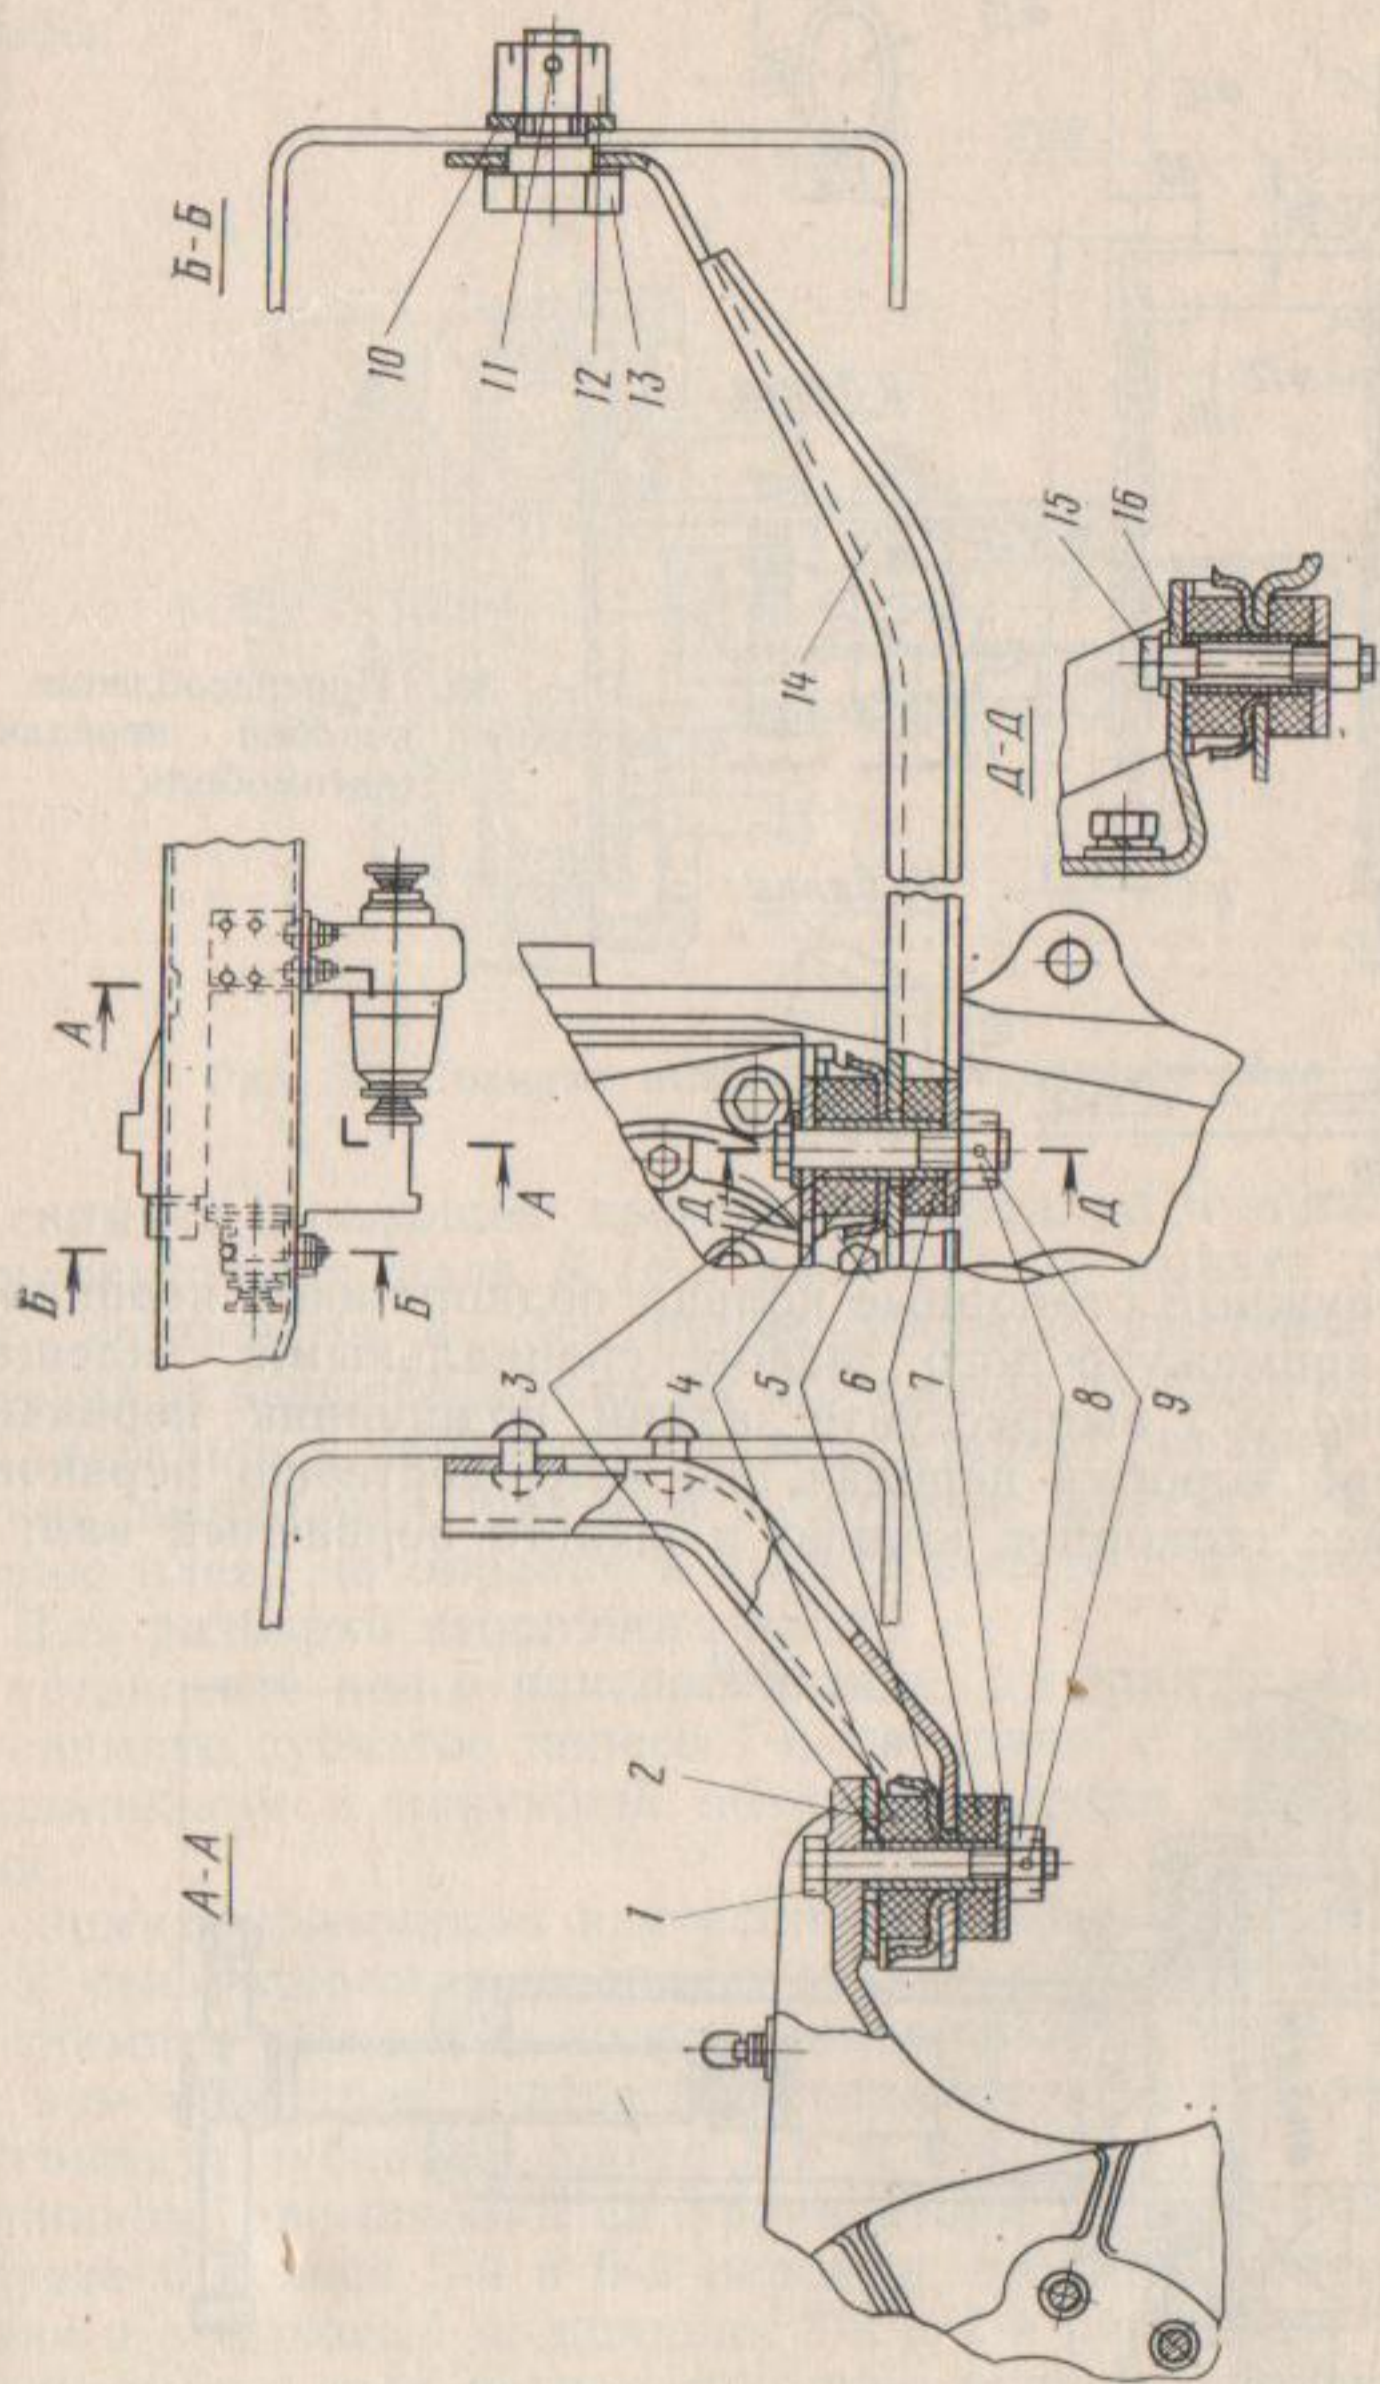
Подвеска коробки передач и раздаточной коробки:
